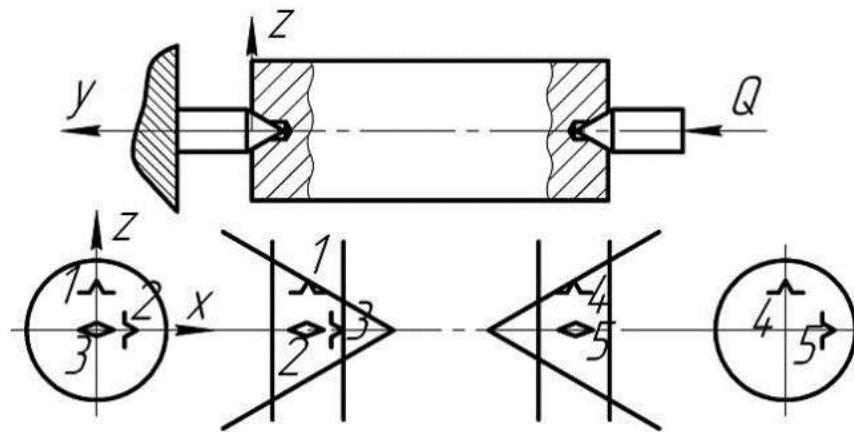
Встановлення заготовки на жорсткий центр.
